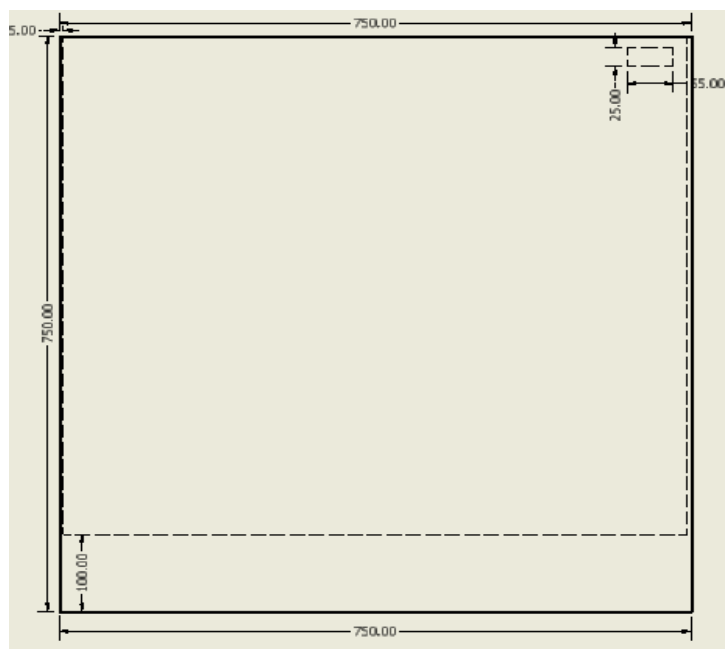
Planos de caja para fermentación de cacao. (Fuente los autores).
